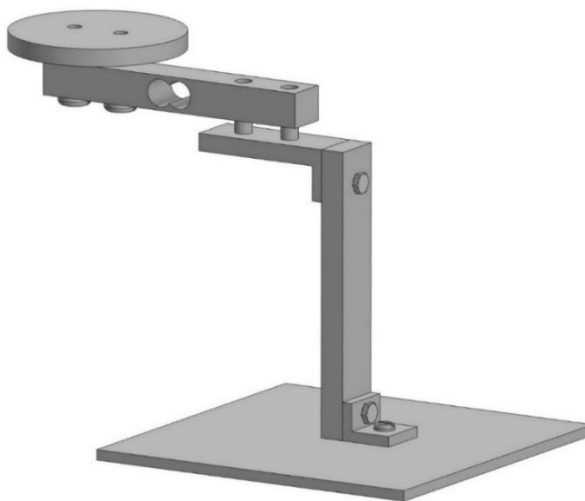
Внешний вид 3D-модели крепления для тензорезистивного датчика.
